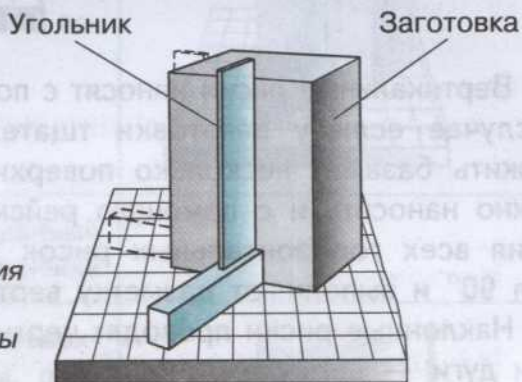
Выверка положения заготовки относительно плоскости разметочной плиты
